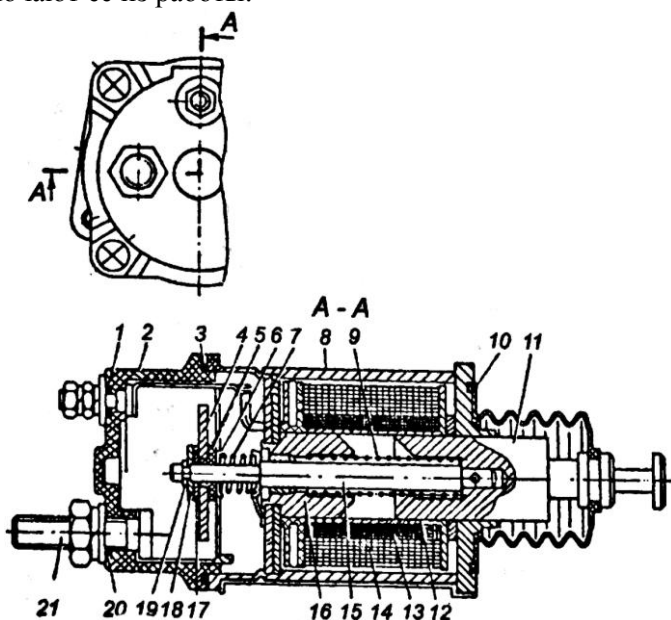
Тяговое реле стартера СТ142-Б с неразделенной контактной системой: 1, 20 – резиновые уплотнительные шайбы; 2 – крышка реле; 3 – резиновое уплотнительное кольцо; 4 – контактный диск; 5 – изоляционная втулка; 6 – чашка; 7, 9 – пружины; 8 – корпус; 10 – резиновый сильфон; 11 – якорь реле; 12 – каркас катушки;
